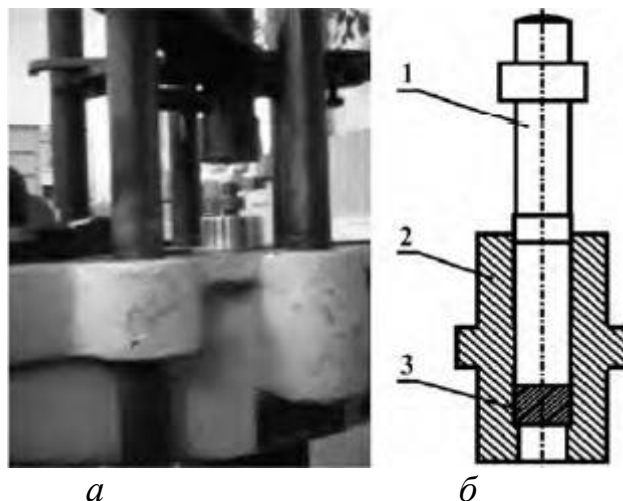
Робоча частина машини УВМ-50 з встановленим пресовим пристроєм (а), пресовий пристрій (б)
